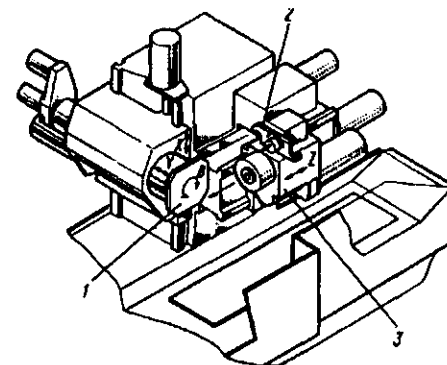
Схема токарно-сверлильно-фрезерно-расточного станка: 1 – палета в рабочей позиции на шпинделе изделия; 2 – манипулятор для смены инструмента; 3 – шпиндельная бабка. Стрелками на рисунке обозначены возможные направления перемещений рабочих органов станка
